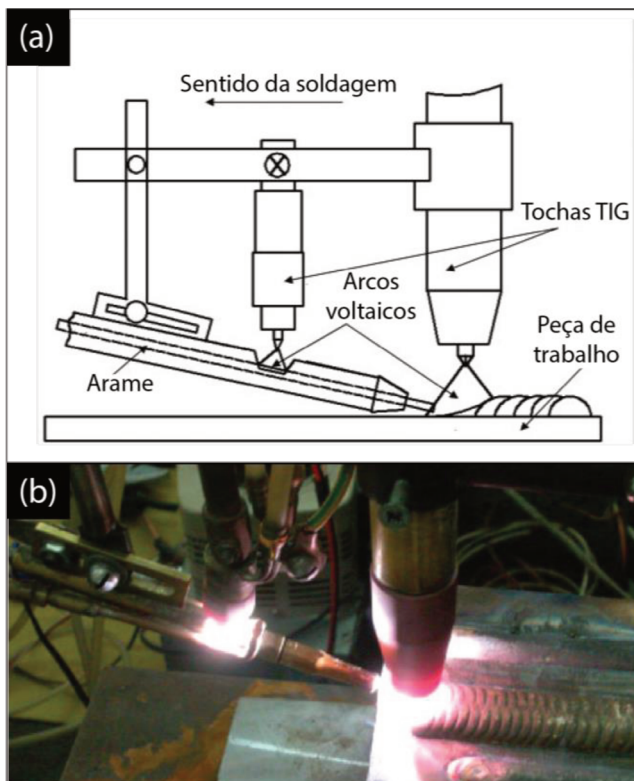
(a) Desenho esquemático da técnica de aquecimento por arco TIG e (b) a aplicação real da técnica. Adaptado de [3]
